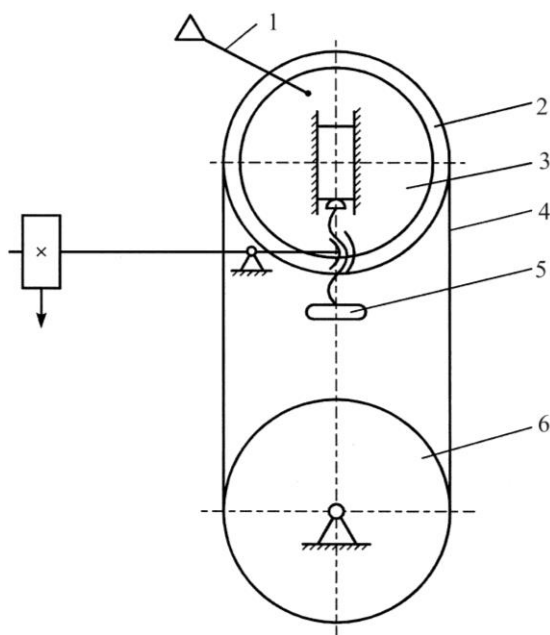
Конструкция узла резания ленточнопильного станка с новой конструкцией ведомого шкива: 1 – воздухопровод; 2 – ведомый шкив; 3 – диск; 4 – пила; 5 – механизм натяжения пилы; 6 – ведущий шкив
